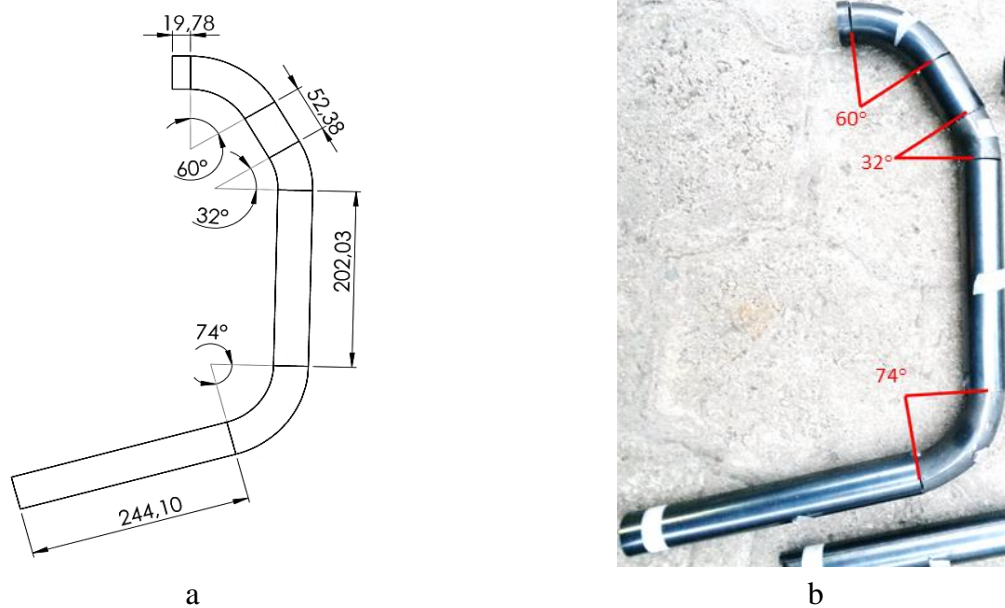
Proceso de ensamblaje de tubería: (a) dimensiones de diseño, (b) construcción
